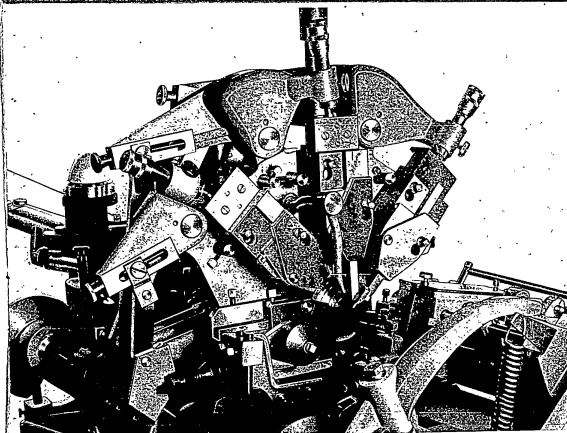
MANCHE PORTE-OUTILS DU TOUR BP-U12
